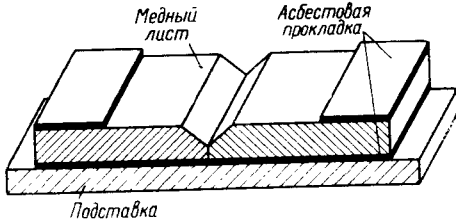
Приспособления против потерь тепла при сварке
